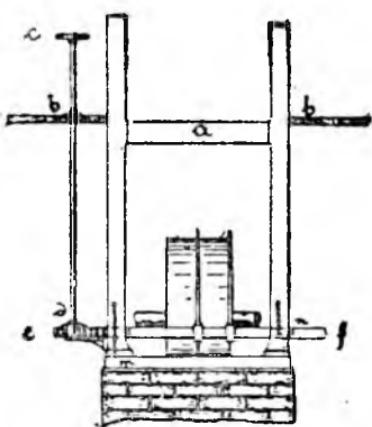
Приспособление для предупреждения неожиданного пуска станка.
